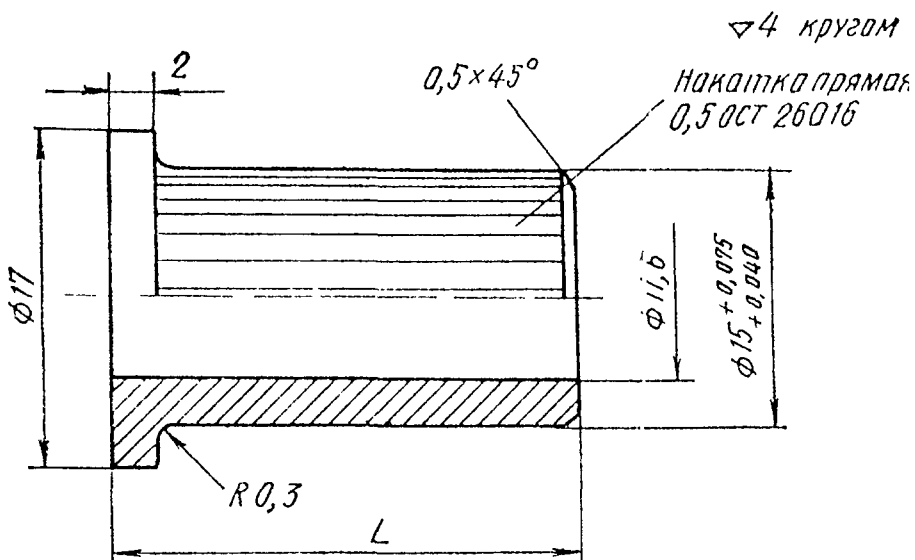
Втулка корпуса и крышки крана 24-7603-900
